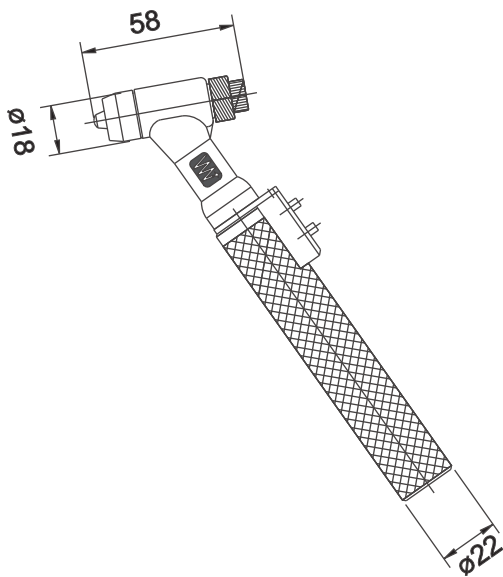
PWH 100 горелка для ручной сварки с кнопкой
